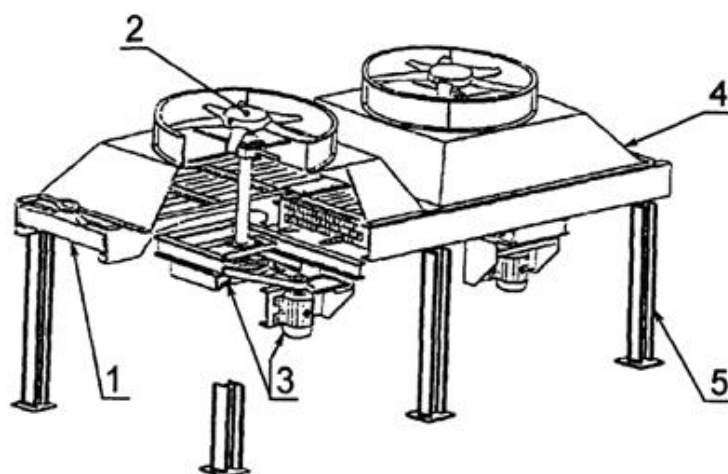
АВО вытяжного вида: 1 – теплообменная секция; 2 – колесо вентилятора; 3 – привод вентилятора; 4 – диффузор с коллектором; 5 – металлоконструкция
